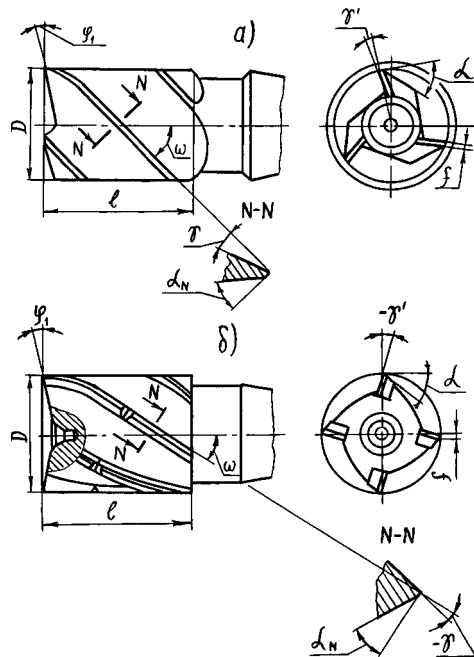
Концевые фрезы: а) из быстрорежущих сталей; б) с винтовыми твердосплавными пластинками
